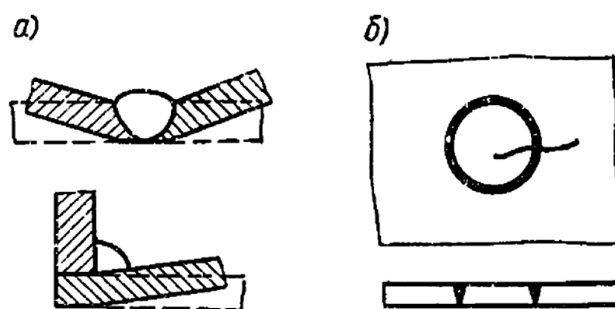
Деформации и напряжения, вызванные неправильной сваркой:
